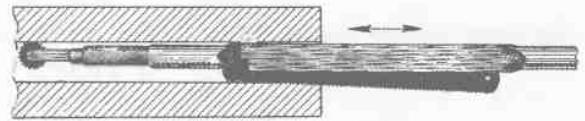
Пила для продольных пазов внутри канала, обеспечивающих сушку древесины внутри заготовки
